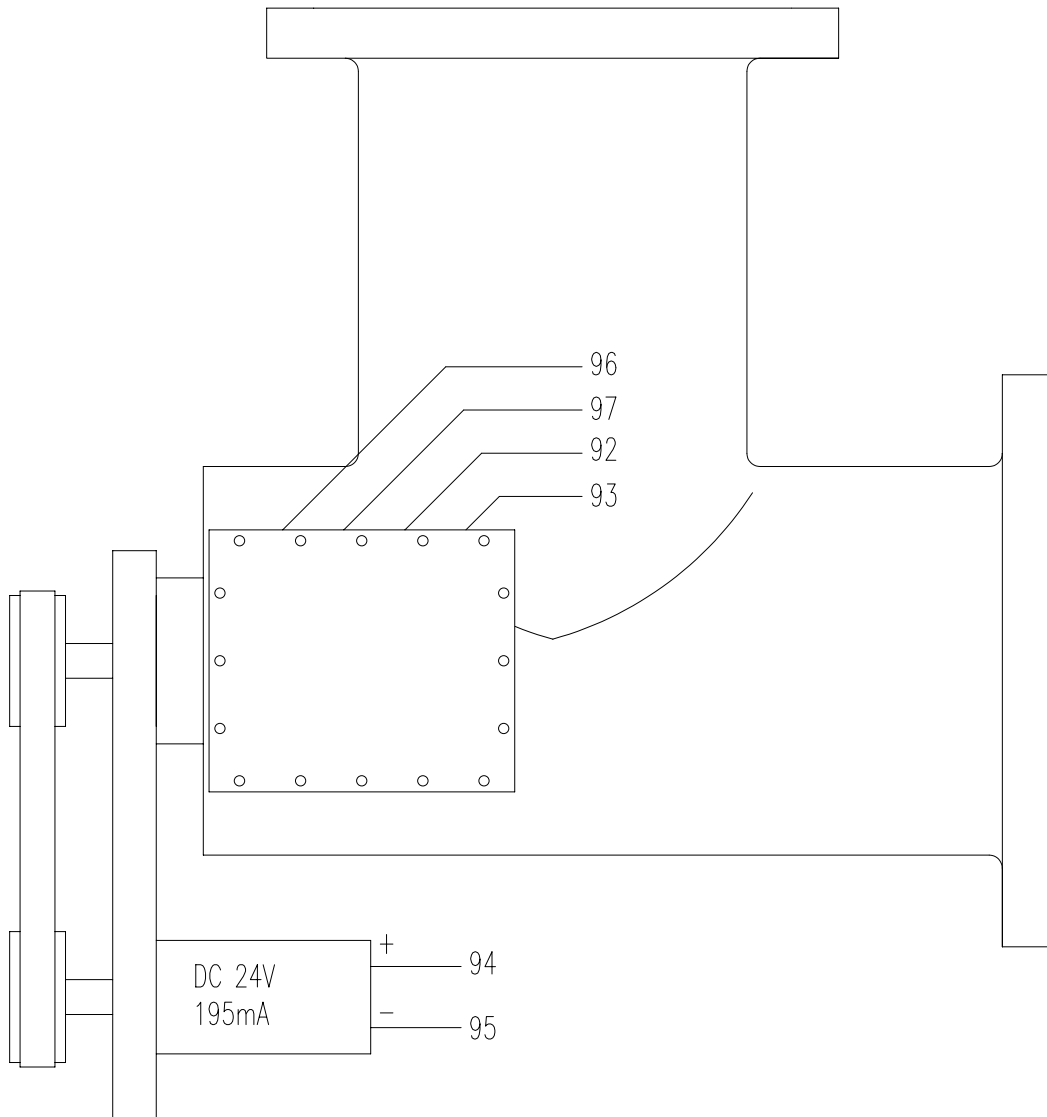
VISTA DI RIFERIMENTO / REFERENCE VIEW
